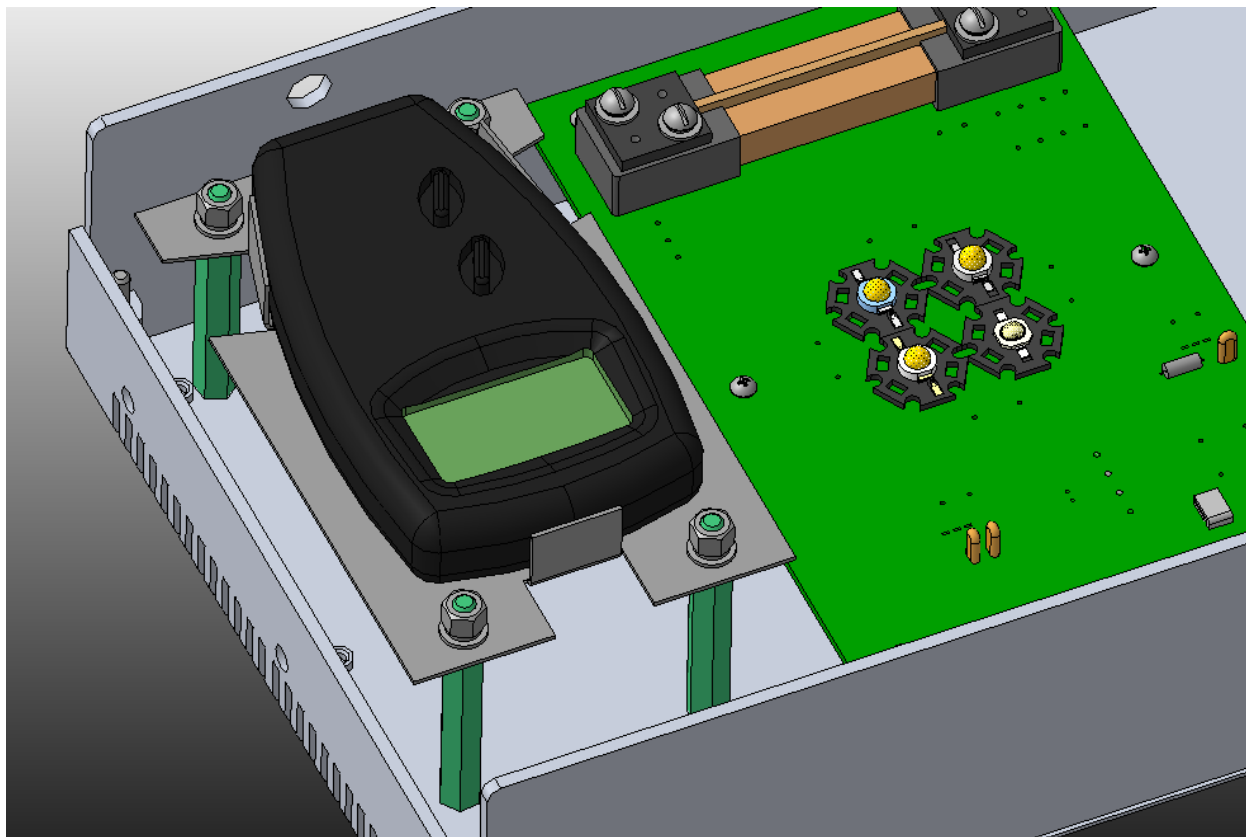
Крепление держателя люксметра к корпусу стенда (крышка корпуса не показана).
